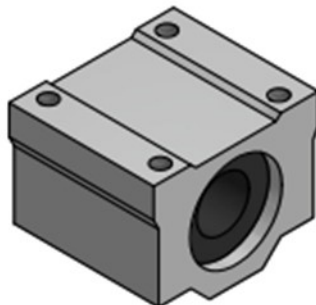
^η : Pillow Block Ball Bearing 8mm
